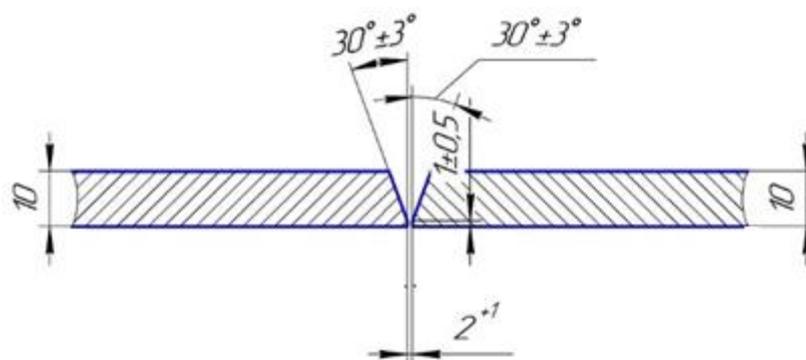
V-образная разделка кромок под сварку С17
